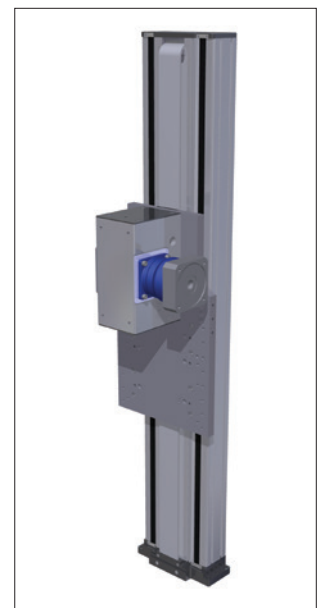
AXDL mit Zahnriemen - Ω - Antrieb
